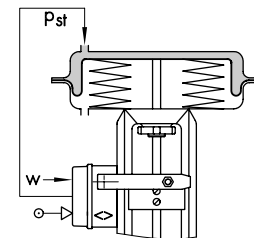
Sentido de actuación << Montaje a la izquierda
